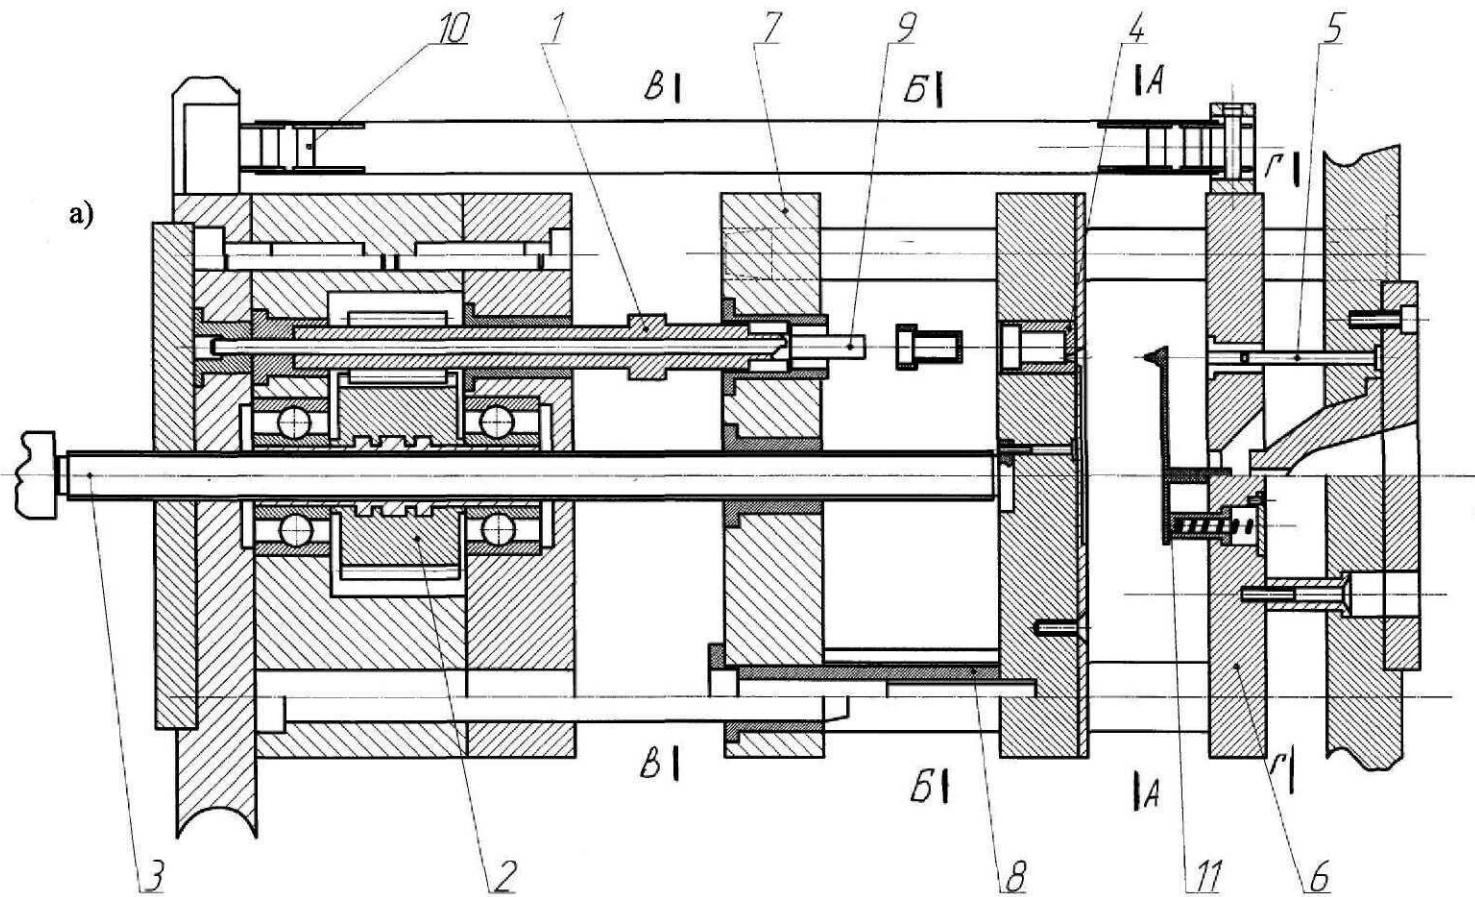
Пресс-форма для изготовления детали «колпачок» с внутренней резьбой:
